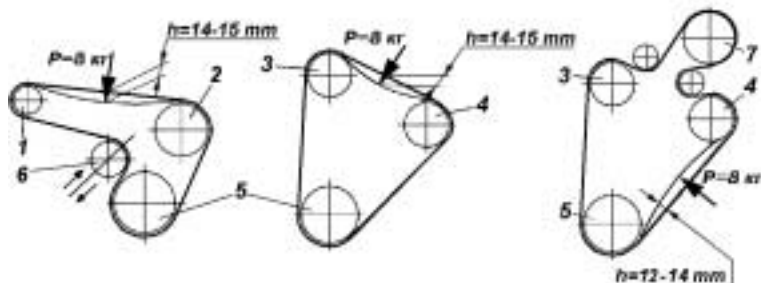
Схема натяжения ремня привода агрегатов:
